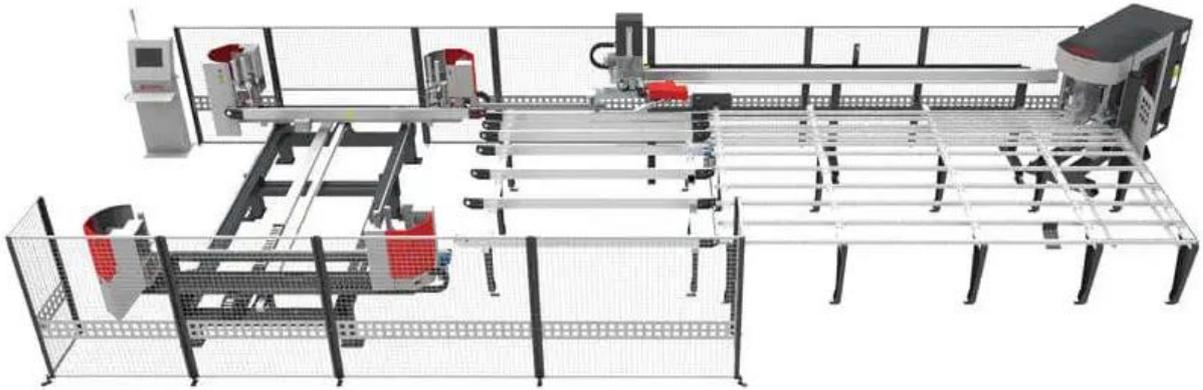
Línea de soldado y limpieza automática KABAN TD 3020
